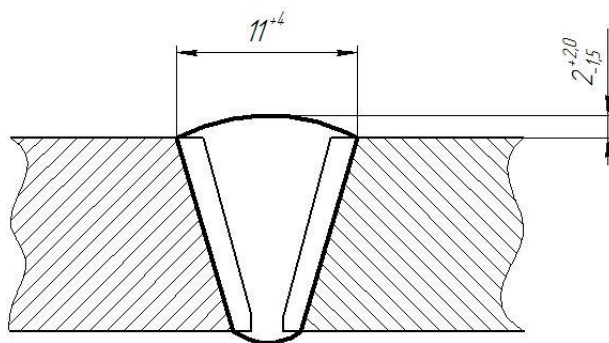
Размеры сварного шва при соединении труб диаметром 325 мм
